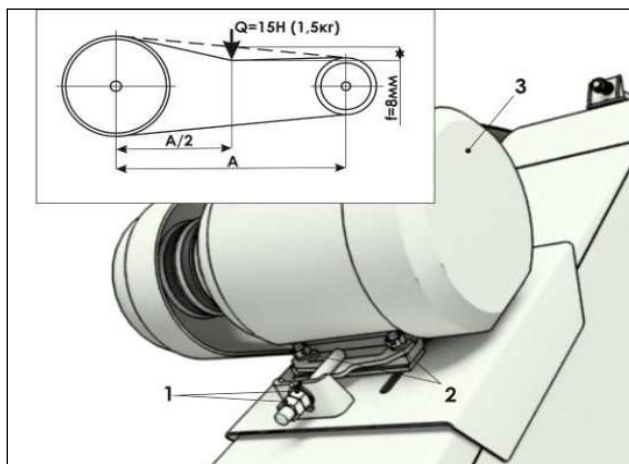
Регулировка натяжения клиноременной передачи привода загрузочного транспортера 1, 2– Гайка; 3 – Электродвигатель
